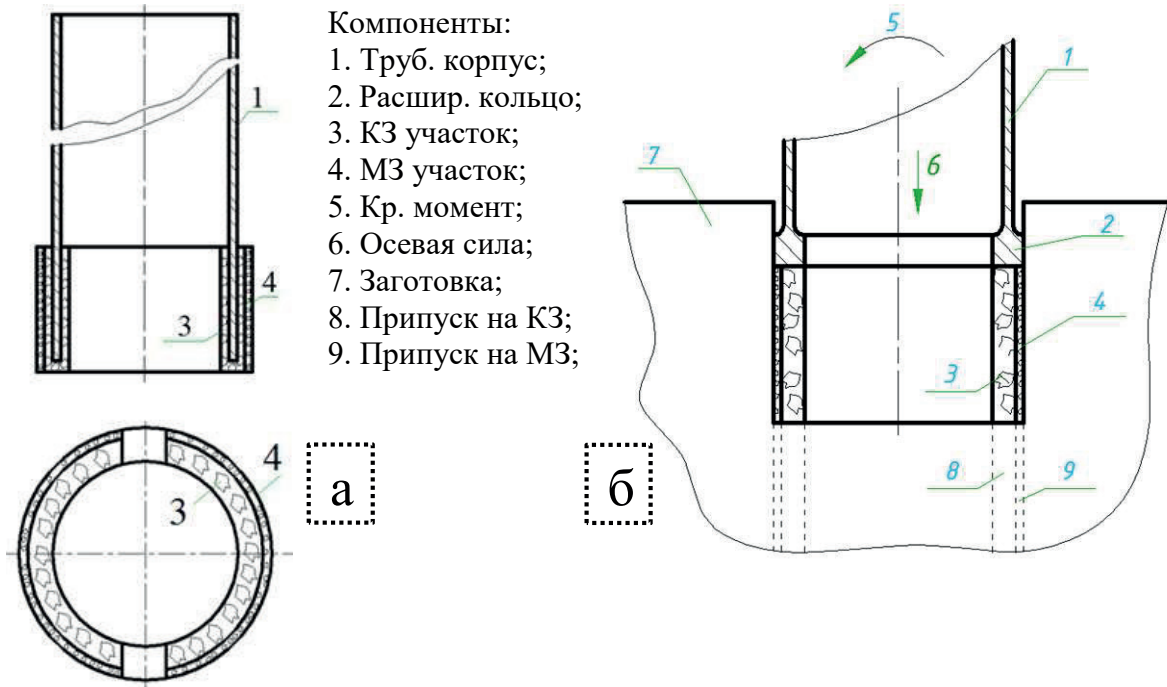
Конструкция двухслойного кольцевого сверла (а) и схема съема припуска (б) [3]
